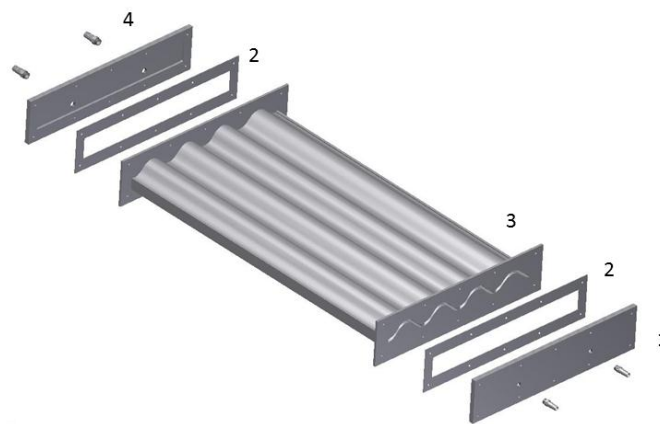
Wellenreaktor – Explosionszeichnung. 1: vordere Stirnplatte mit ½“ Schlauchtülle; 2: 3 mm Silikondichtung; 3: Hauptreaktorkammer; 4: hintere Stirnplatte mit ¾“ Schlauchtülle.
